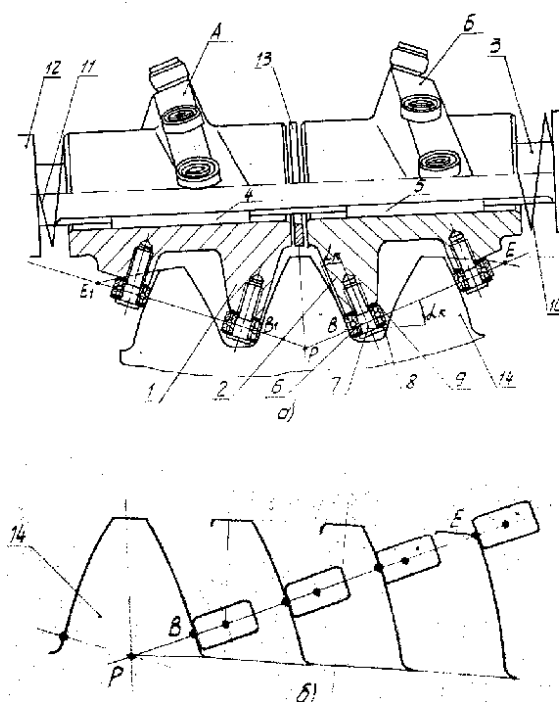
Черв'ячний накатник для обробно-зміцнюючої обробки зубчастих коліс ППД
